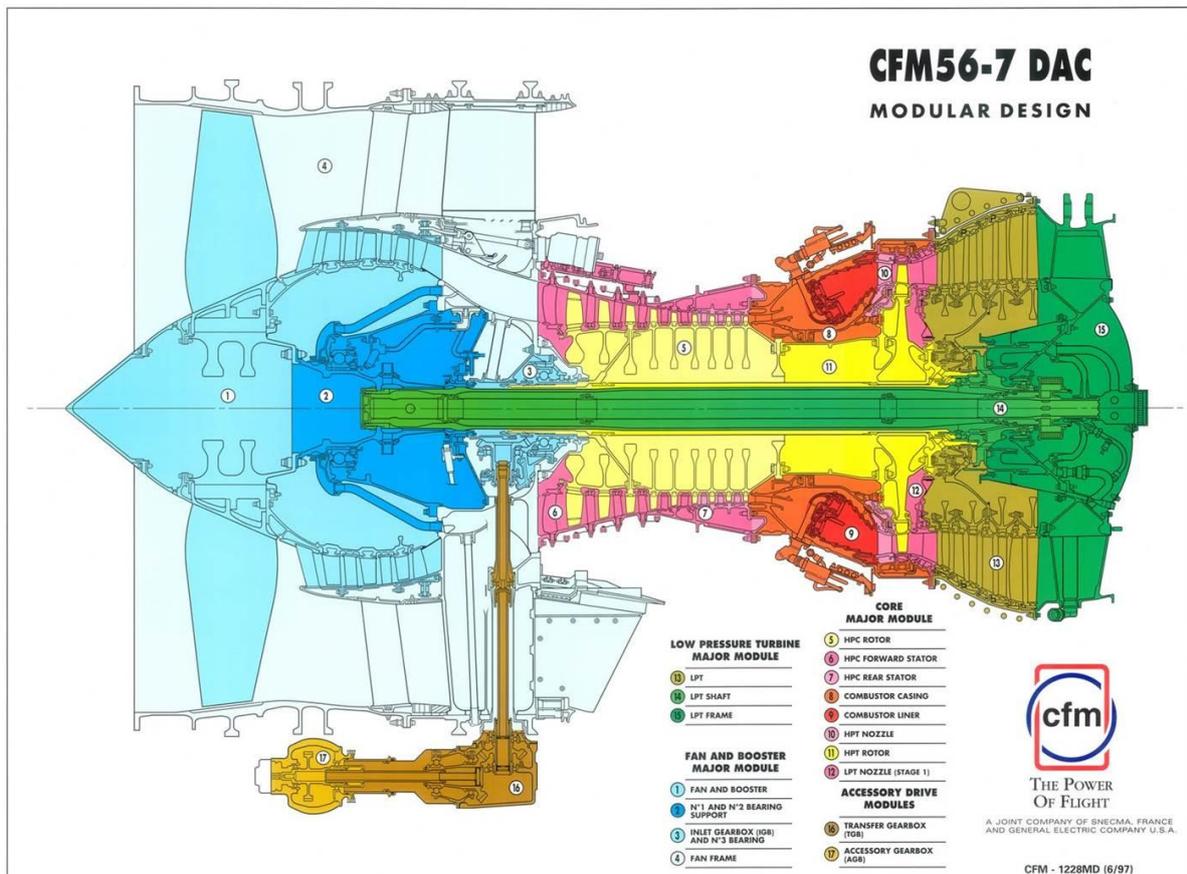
Vue en coupe du moteur CFM56-7B [6]
